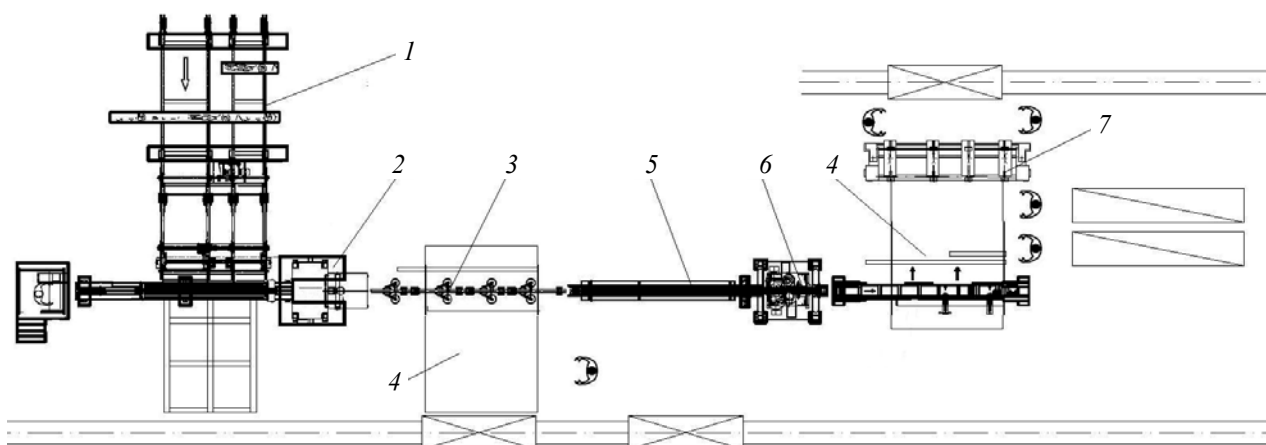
Схема лесопильного цеха для получения полетных заготовок:
